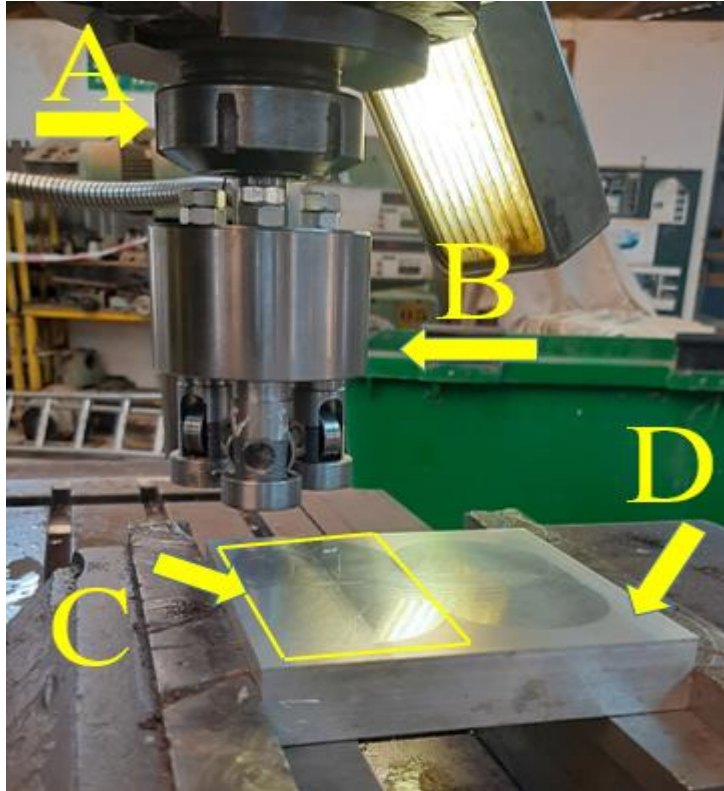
Montage expérimental du procédé de galetage : A- porte outil ; B- outil de galetage ; C- zone galetée ; D- pièce aluminium.
